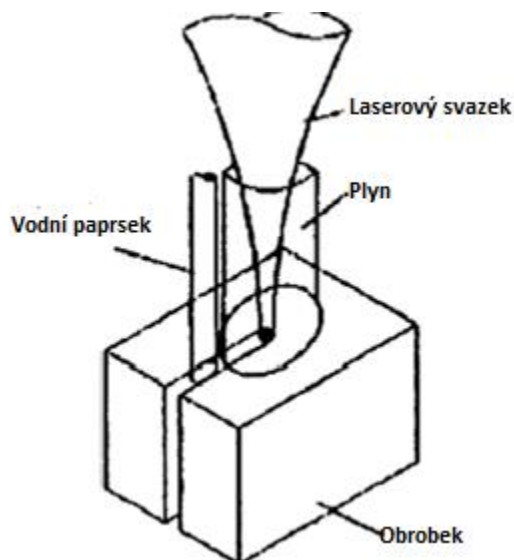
Možné metody kontaktu obrobku s kapalinou při obrábění (převzato z [1])
